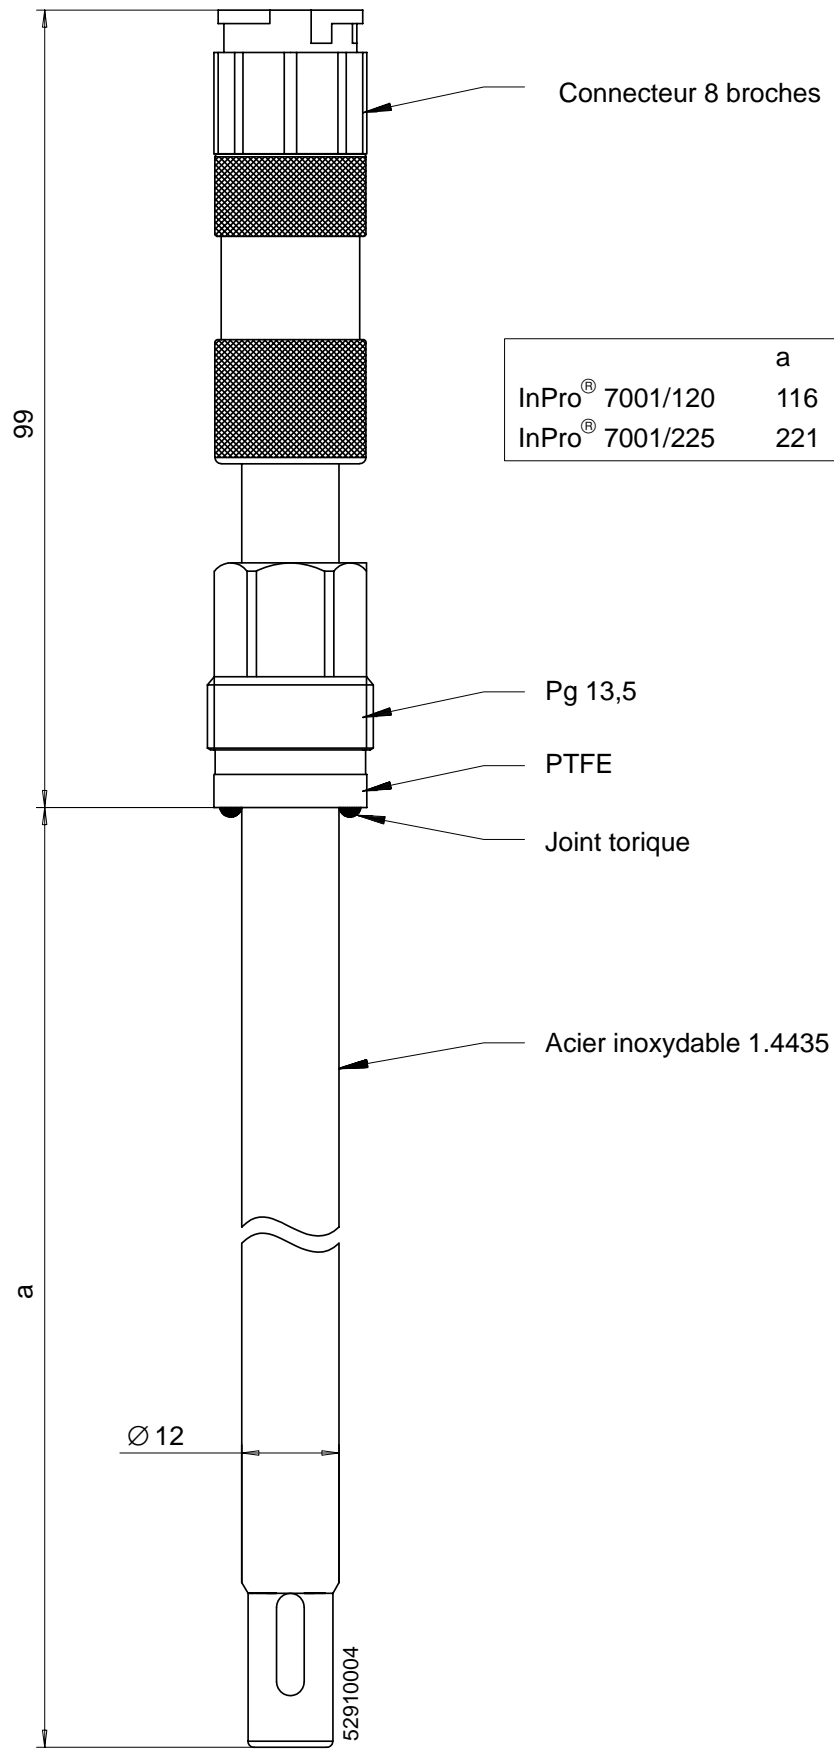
Dessin d'encombrement InPro[®] 7001
